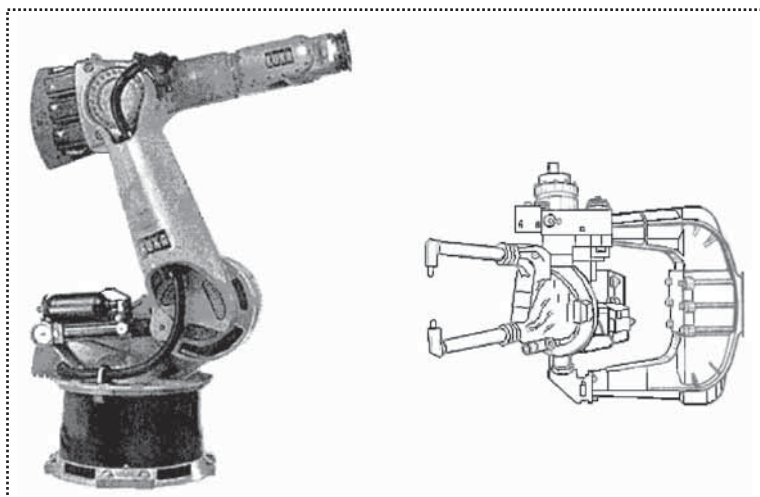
Внешний вид сварочного робота KR-200 фирмы "Kuka" (сварочные клещи сняты)
